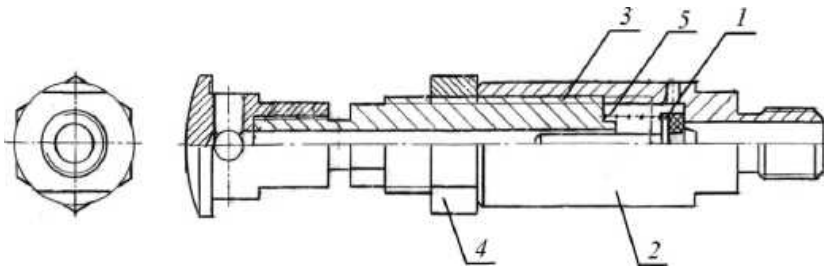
Клапан: 1 – шток; 2 – корпус; 3 – винт; 4 – гайка; 5 – пружина
